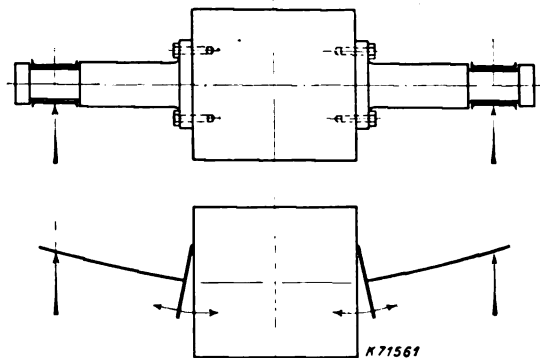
Läuferkörper mit angeflanschten Wellenenden. Schema der Beanspruchung der Flanschschrauben.
